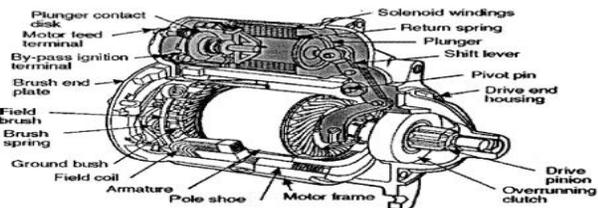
Esquema 2 de um motor de arranque moderno com os elementos para engrenagem a sombreado.
